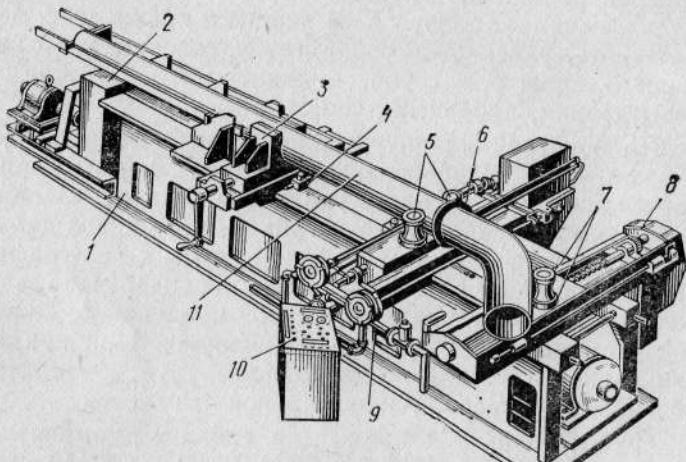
Станок для гибки труб с нагревом ТВЧ типа ТГУ-325
